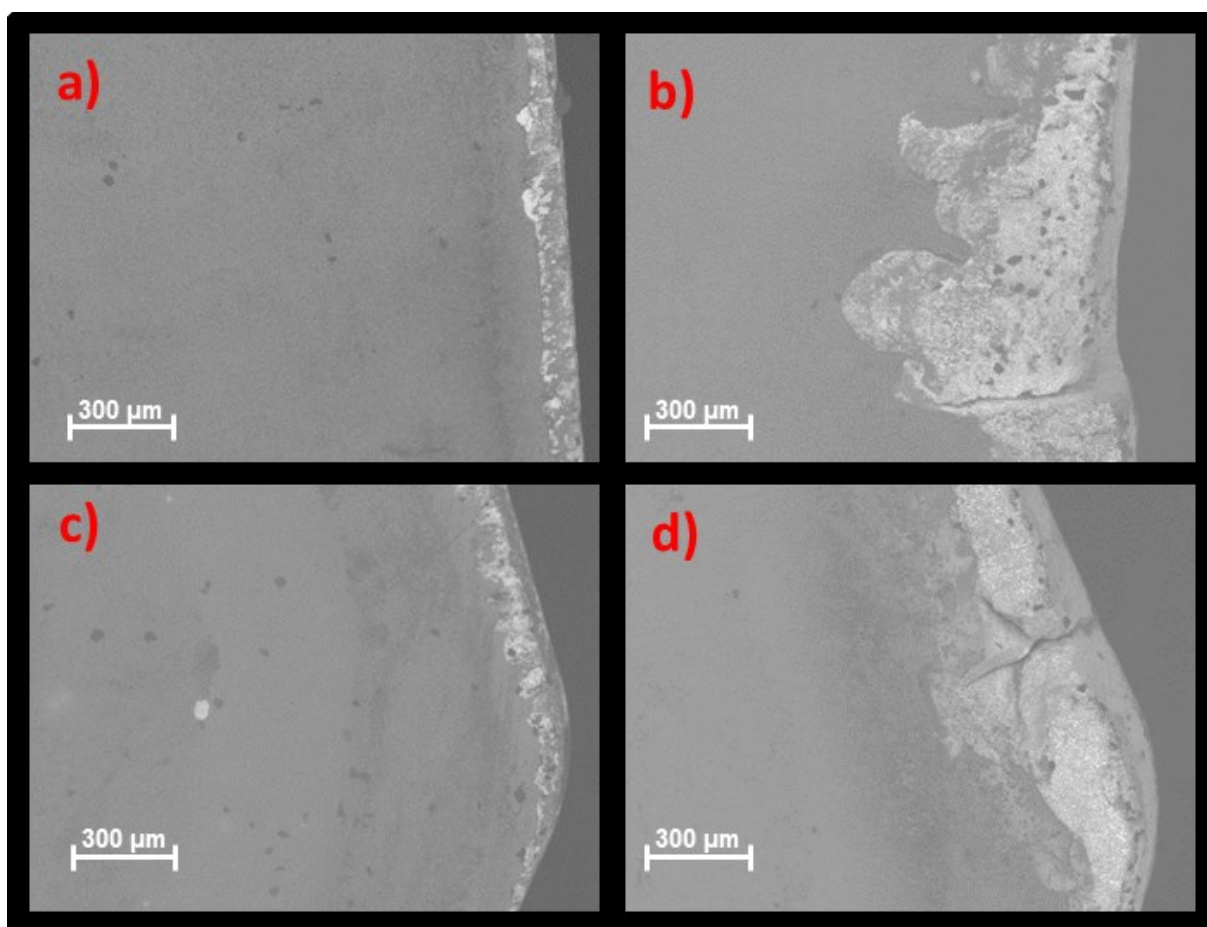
Fotos dos desgastes das ferramentas revestidas de TiN após usinar o CGI A com MQL. a) Desgaste de flanco na usinagem da peça com pre-furos; b) desgaste de flanco na usinagem da peça maciça; c) desgaste de cratera na usinagem da peça com pre-furos; d) desgaste de cratera na usinagem da peça maciça.
